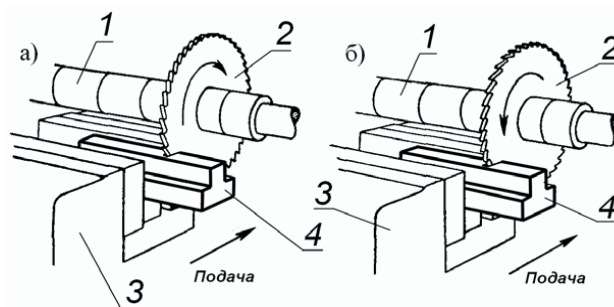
Класична схема розпилювання матеріалу дисковою пилою: а – проти подачі; б – за подачею, де 1 – приводний вал; 2 – дискова пила; 3 – затискне пристосування; 4 – заготовка
